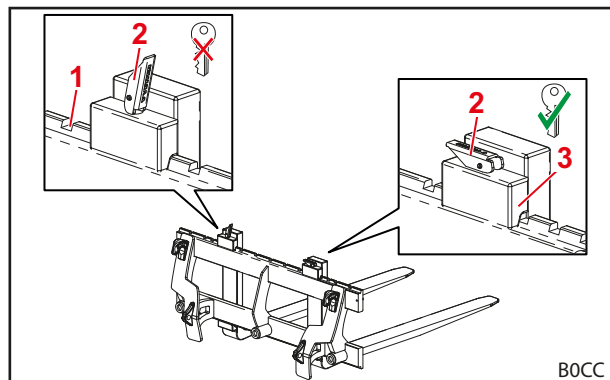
Vergrendeling van de pallettanden (links – geopend, rechts – gesloten)
